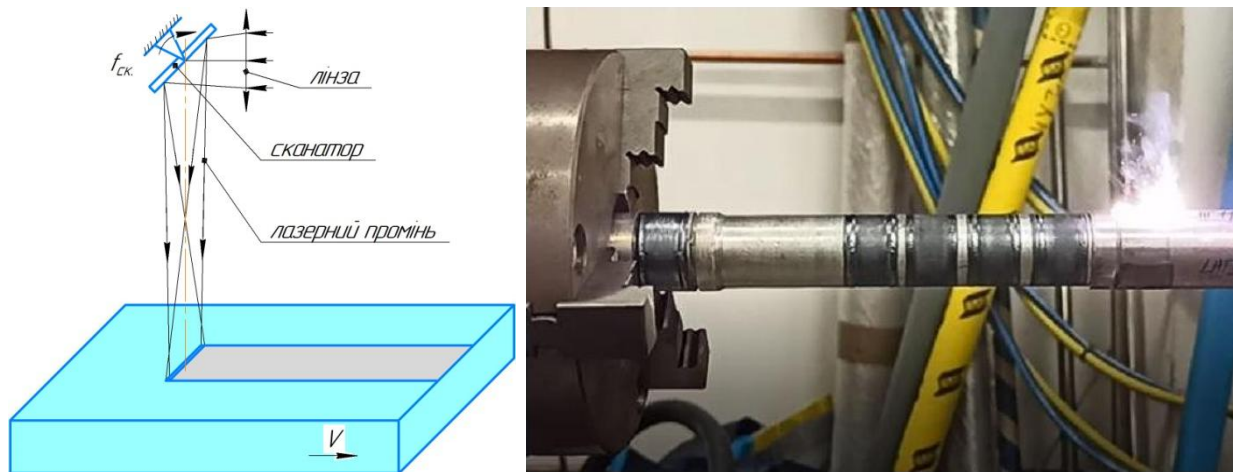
Схема лазерної поверхневої термообробки
